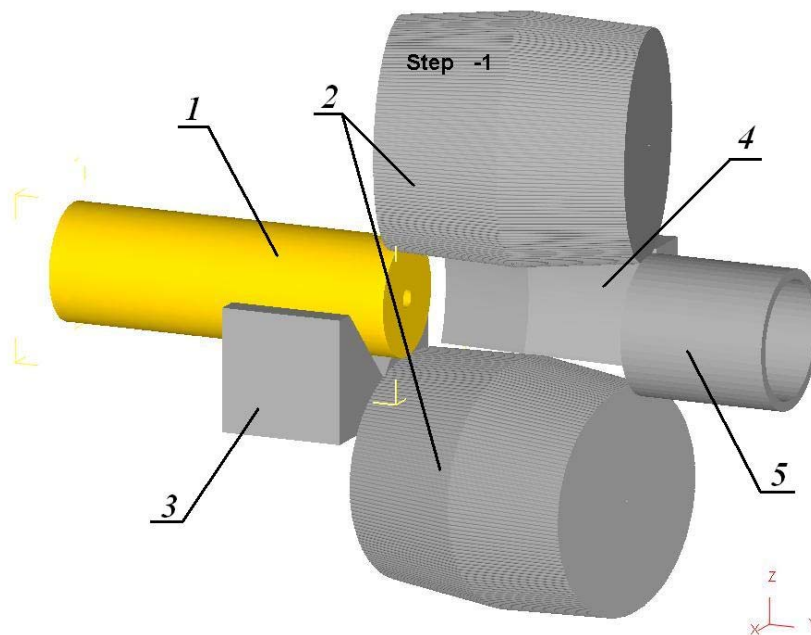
Очаг деформации двухвалкового стана винтовой прокатки: 1-заготовка; 2-рабочие валки; 3-удерживающий желоб; 4-направляющие линейки; 5-выходное кольцо.
